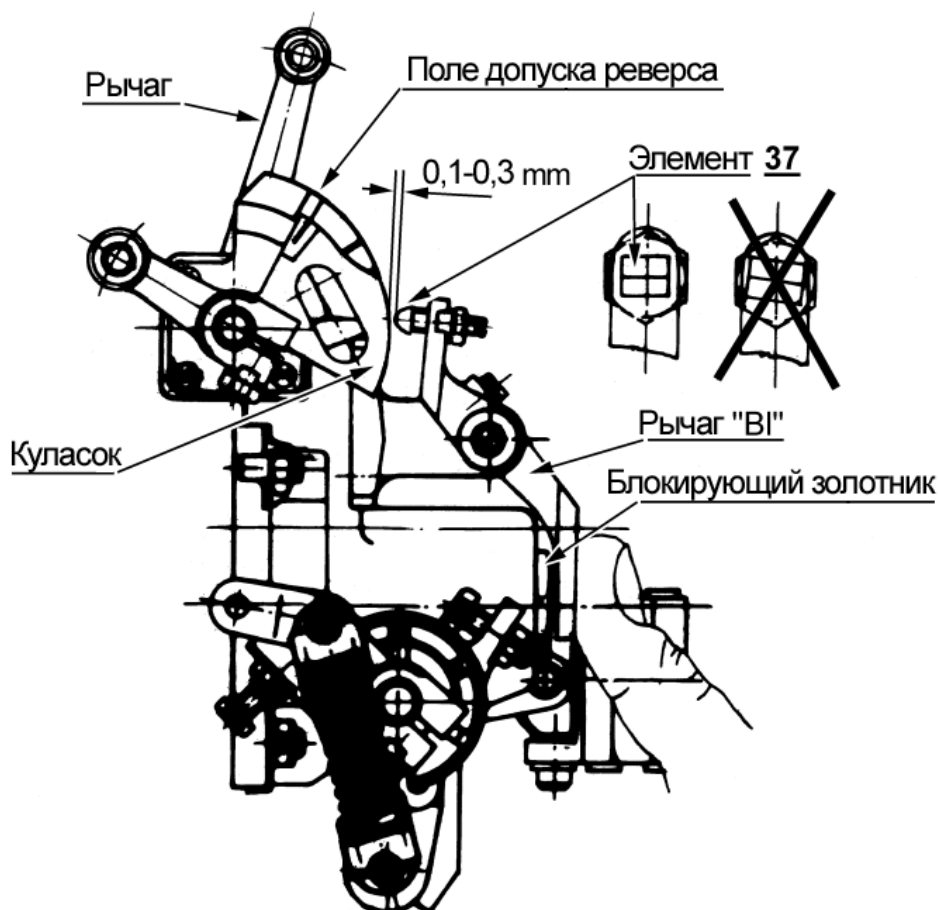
Регулировка осевого зазора блокирующего золотника
